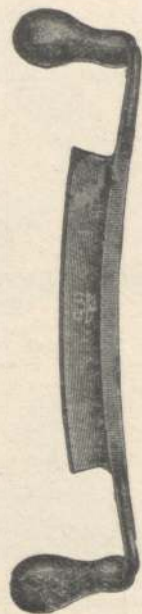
Das geschweifte Schneid- oder Zugmesser.
